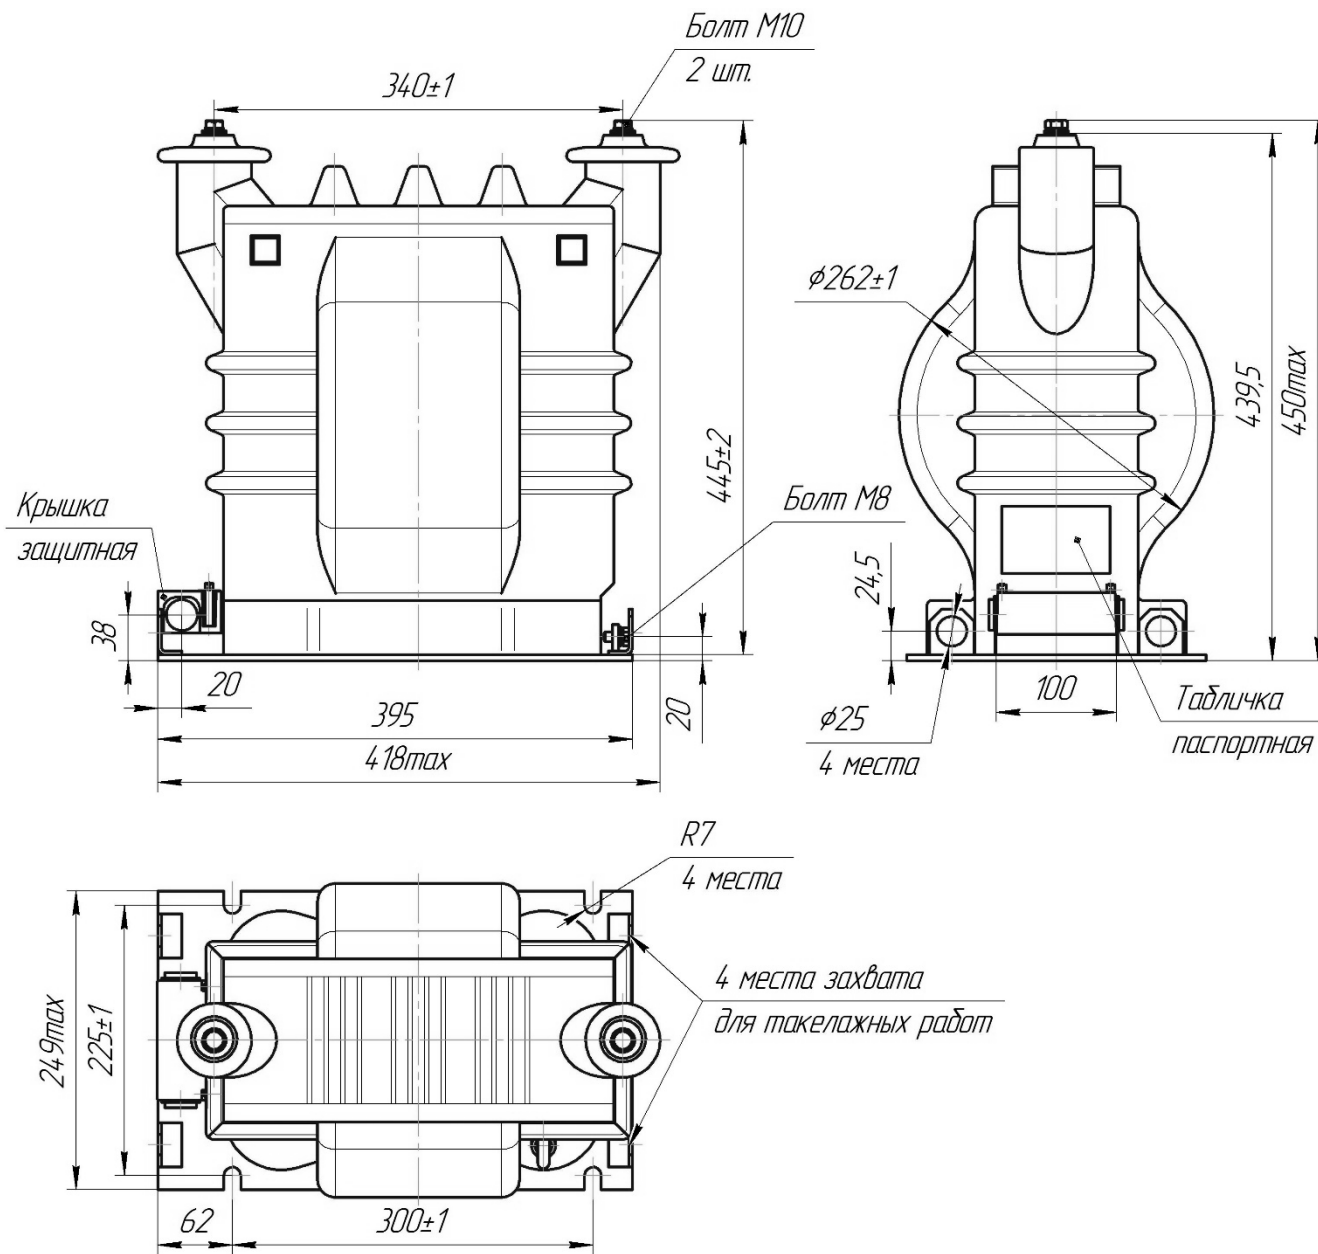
Габаритные, установочные и присоединительные размеры трансформаторов напряжения НОЛ-СЭЩ-20
